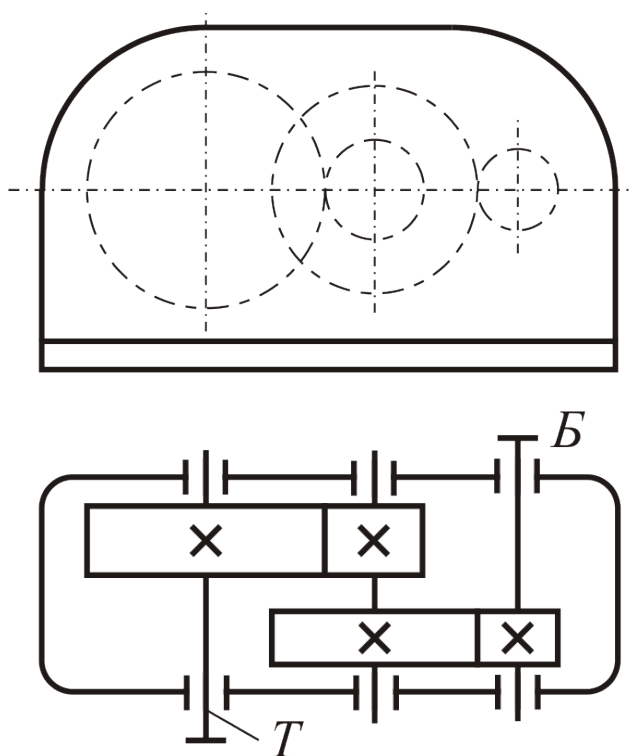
Кинематическая схема двухступенчатого горизонтального редуктора с цилиндрическими колесами
